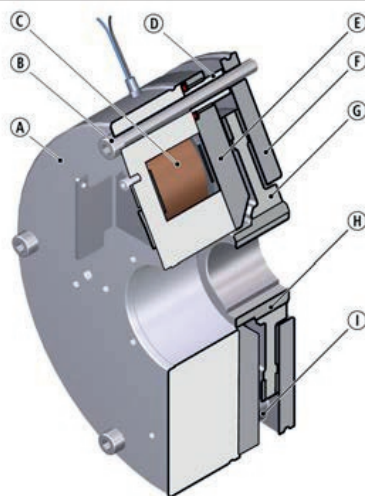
Aufbau einer Federkraftbremse INTORQ BFK464-□R: Magnetteil komplett + Rotor + Flansch
